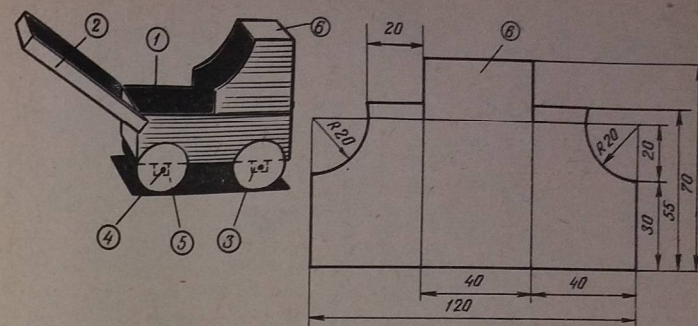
Модель детской коляски: 1—корпус; 2—ручка; 3—подшипник; 4—ось; 5—колесо; 6—тенд
